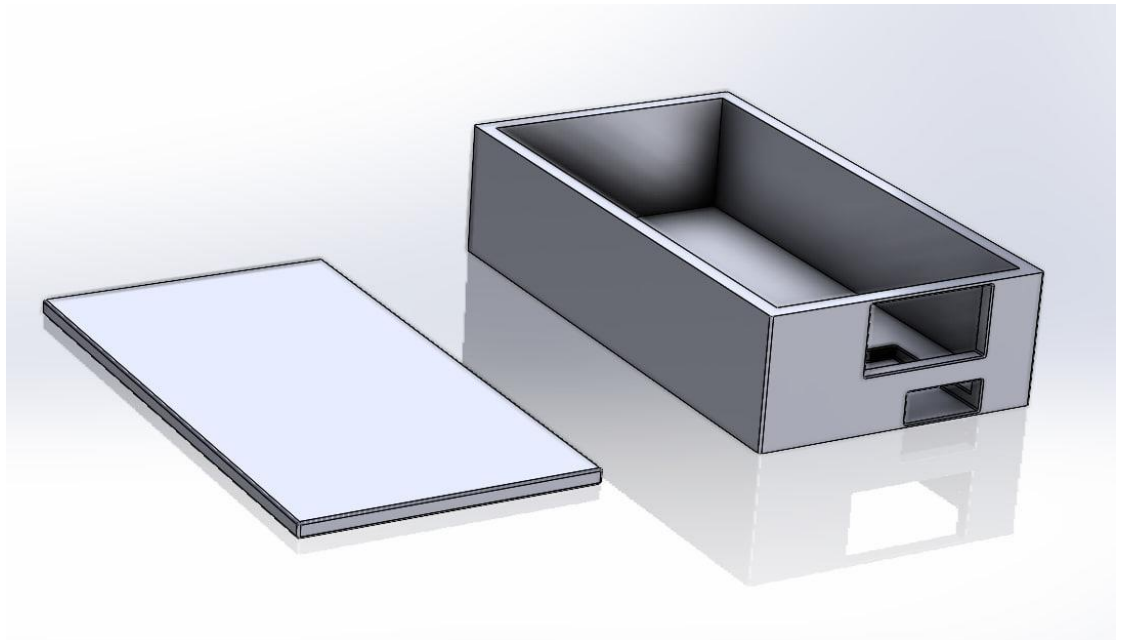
3D модель корпусу для акумуляторного блоку
